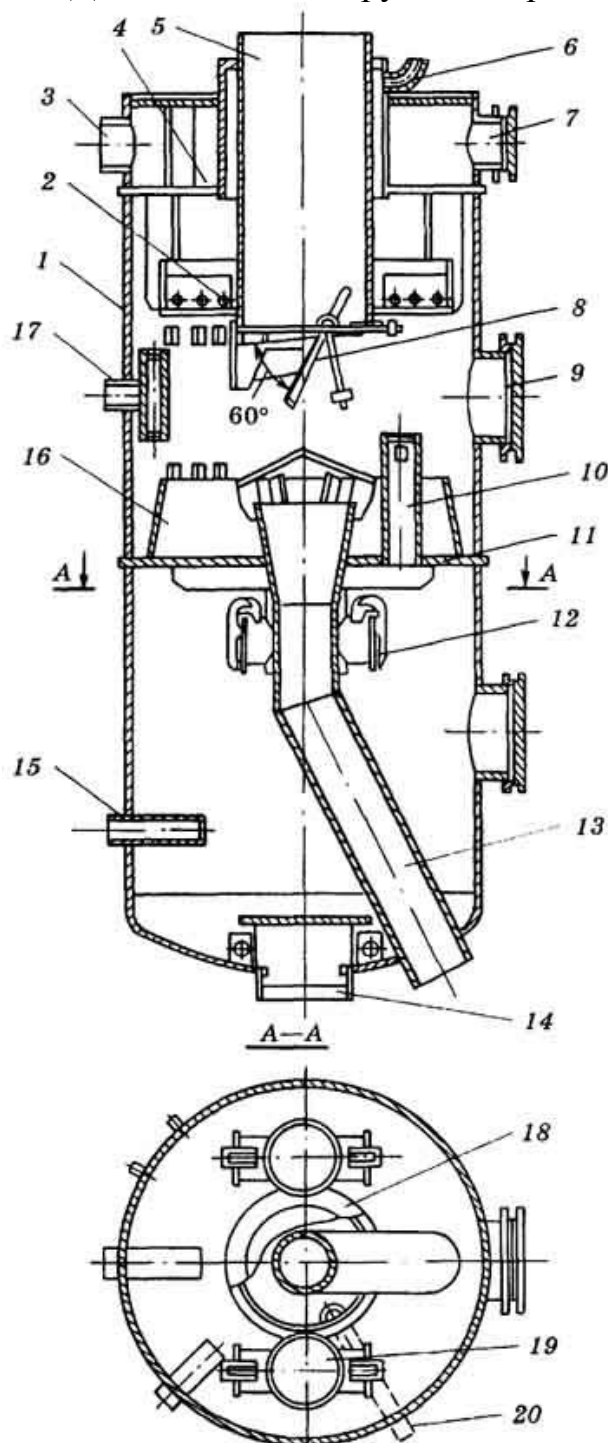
Схема конструкции вертикального смешивающего подогревателя: 1 – корпус; 2, 4 – дырчатые листы; 3 – линия подвода конденсата; 5 – подвод пара; 6 – отсос паровоздушной смеси; 7, 9 – лаз; 8 – обратный затвор для пара; 10 – уравнительная труба; 11 – разделительная перегородка; 12 – обратный затвор для конденсата; 13 – переливная труба; 14 – отвод конденсата; 15 – дренаж из сетевых подогревателей; 16 – переливное устройство; 17 – подвод пара из уплотнений;
